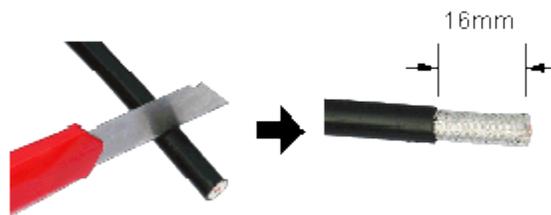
Retirar la cubierta del cable y la capa aislante. Extraído de [11]
